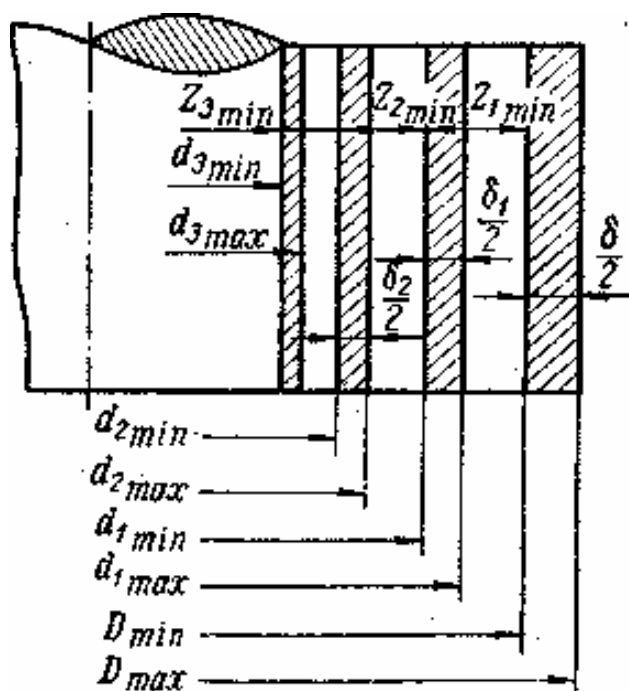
Схемы полей промежуточных припусков и предельных размеров заготовки для черновых и чистовых операций
